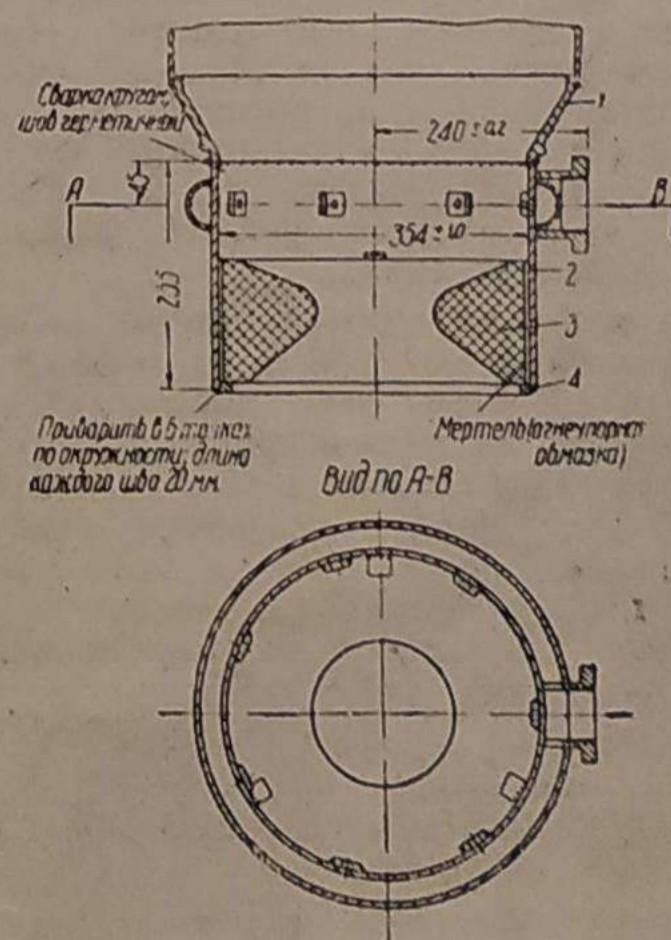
Третий способ восстановления камеры газификации путем приварки полутрубы снаружи камеры.
